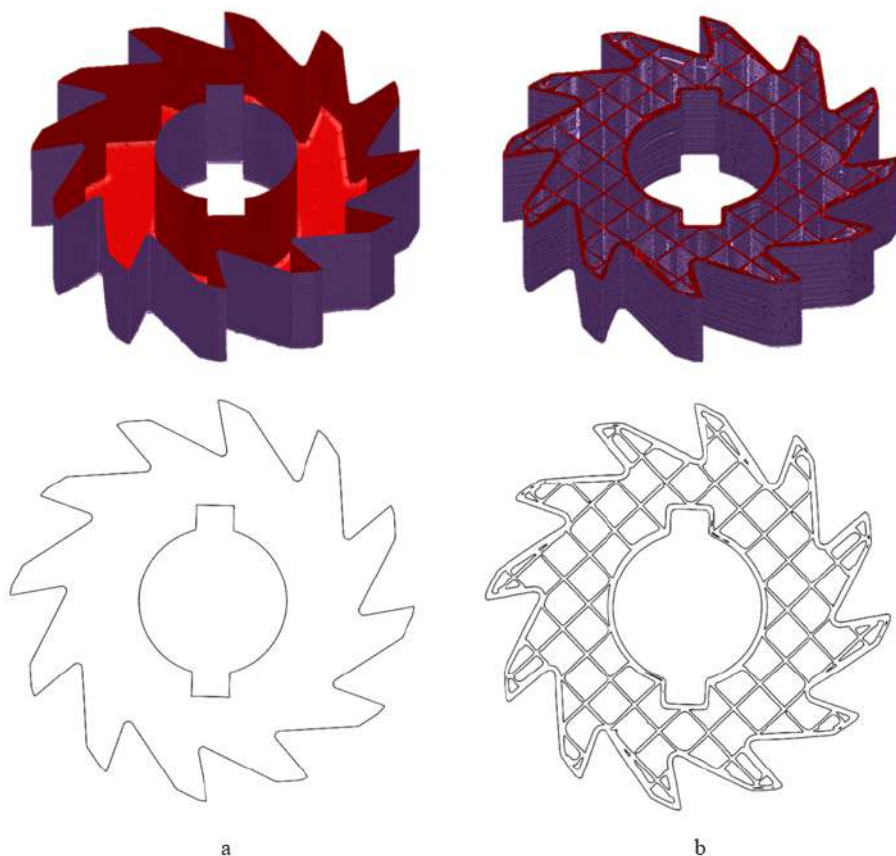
Polygonálny 3D model čelnej valcovej frézy vyrobenej technológiou FDM
